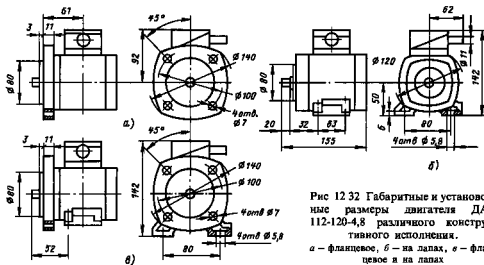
Габаритные и установочные размеры двигателя ДАТ 112-120-4,8 различного конструктивного исполнения. а — фланцевое, б — на лапах, в — фланцевое и на лапах
